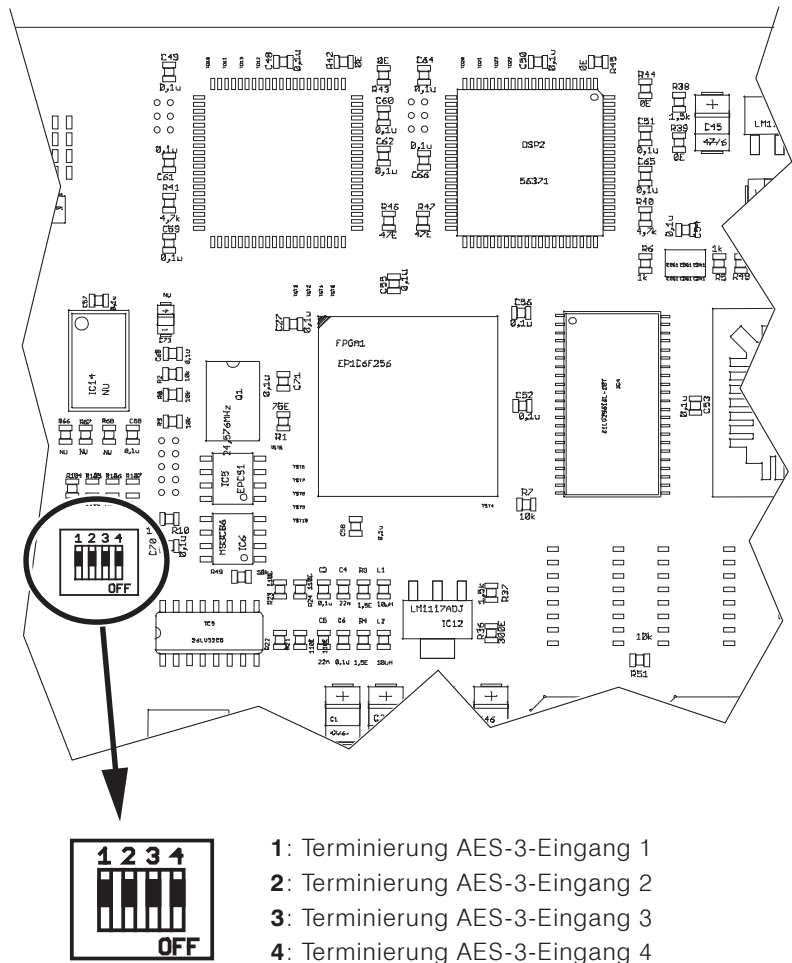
Teilansicht der Hauptplatine mit DIP-Schalter
